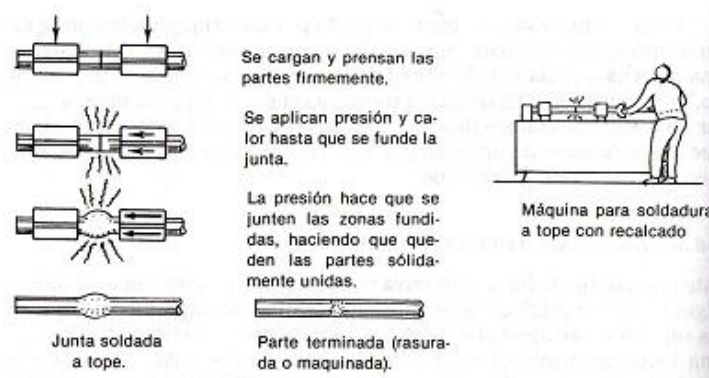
Operación típica de la soldadura a tope con recalcado, utilizada con permiso de Mc-Graw-Hill Company.
